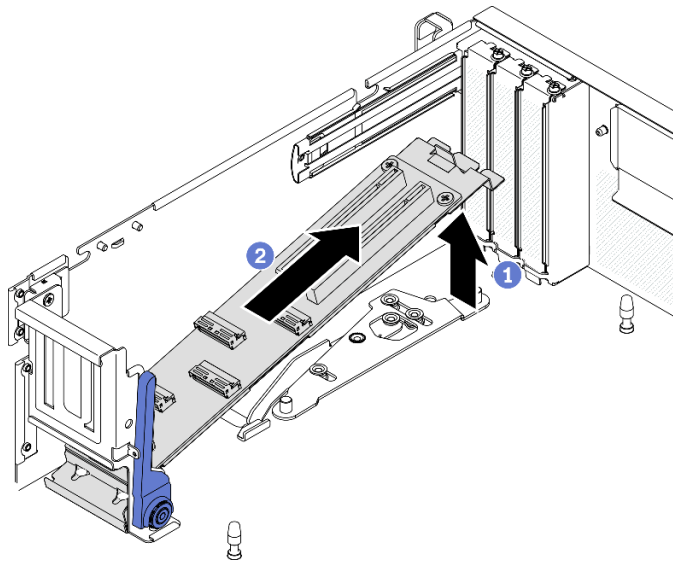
Removendo o módulo de placa de expansão de E/S frontal
